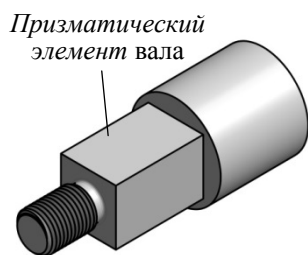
Квадратный хвостовик с резьбовым концом под гайку
